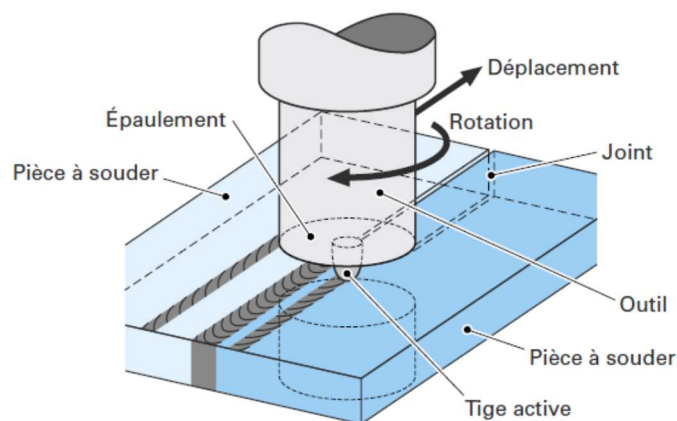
Principe du soudage par friction-malaxage [4].
